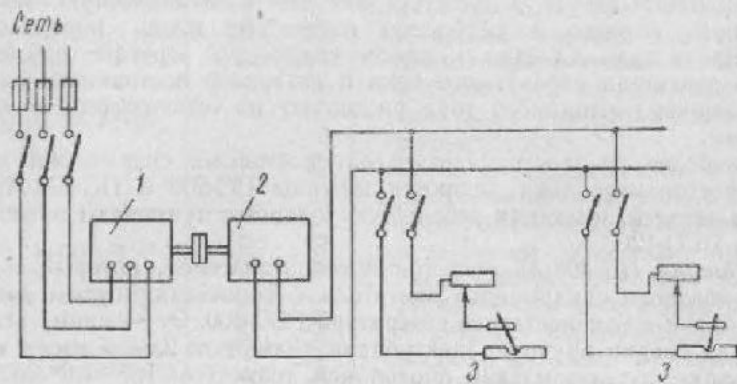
Схема многопостовой сварочной машины ПСМ-1000.
